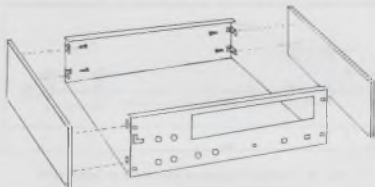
Vista da montagem das laterais de madeira no chassis metálico.
